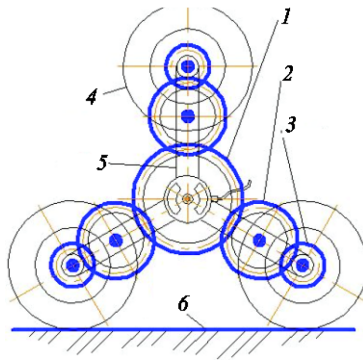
Схема колесно-шагающего движителя: 1 — солнечная шестерня (ведущая); 2 — сцепленный сателлит; 3 — сателлит, приводящий колесо; 4 — колесо; 5 — водило; 6 — опорное основание
